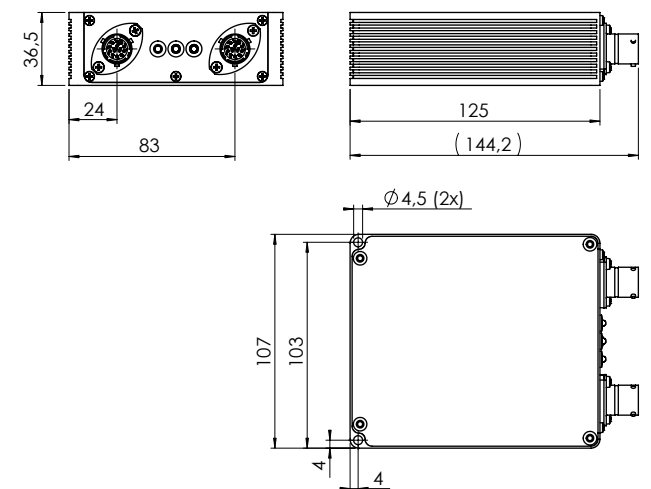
Abmessungen Correvit S-175 Racing Elektronik
